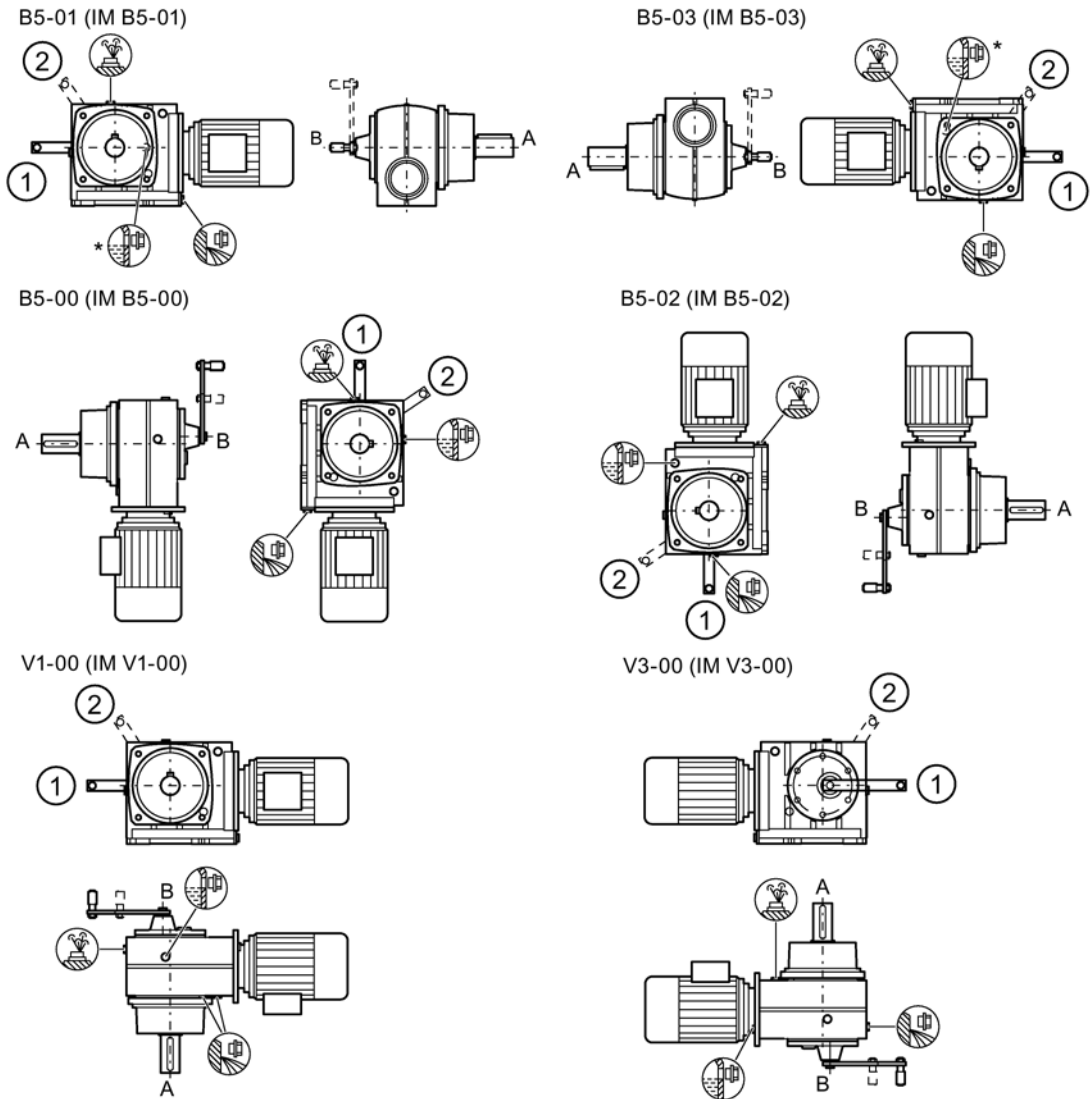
Bauformen für CHZ48, CHF48, CHF68
